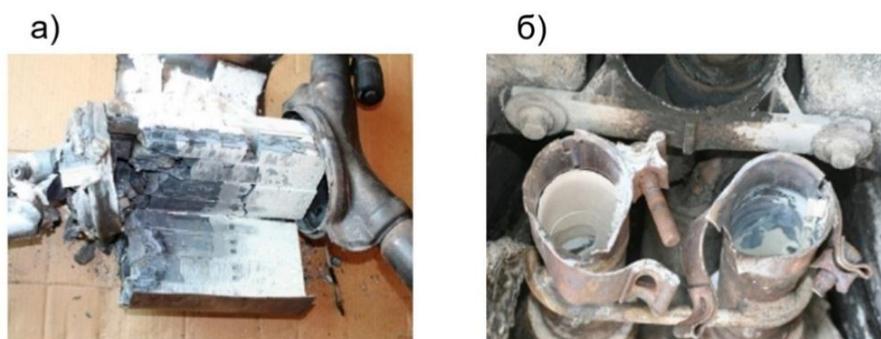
а – поврежденный керамический сотовый блок ДСФ;
